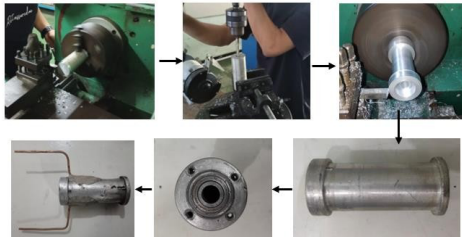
Disain Housing Shaft Micro Turbojet Aero-16
